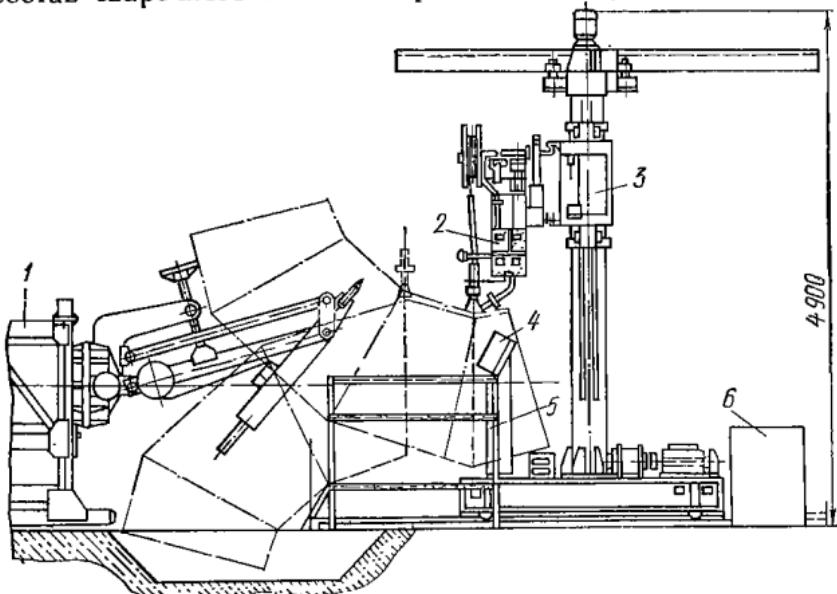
Сварочный пост при изготовлении отводов диаметром 630—1420 мм:
